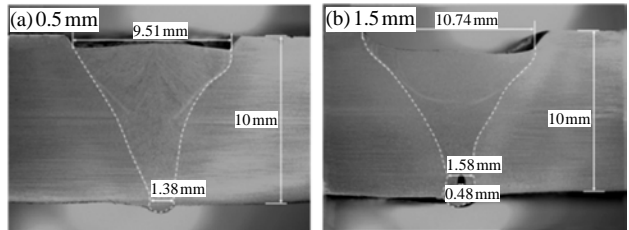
不同装配间隙条件下 K-TIG 焊接接头截面图
